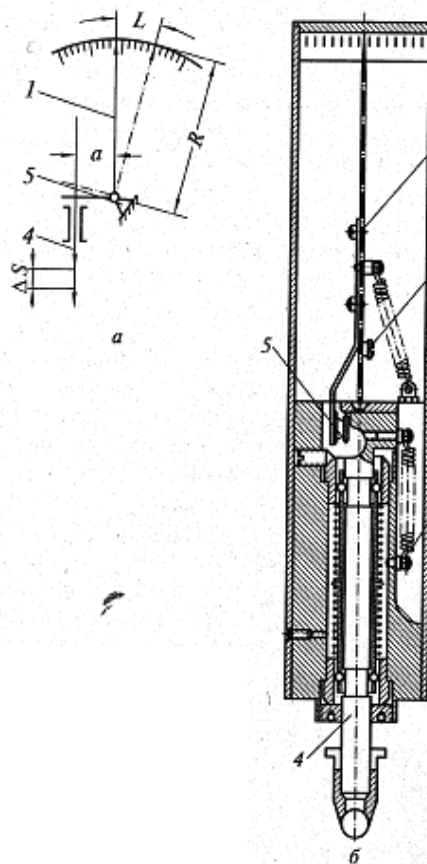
Схема рычага (а) и конструкция (б) миниметра: 1 — указательная стрелка; 2 — регулировочный винт; 3 — пружина; 4 — измерительный стержень; 5 — опорный нож
